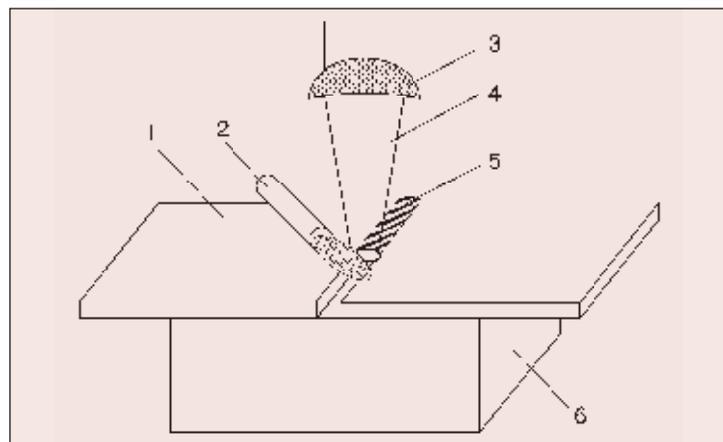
Технологическая схема лазерной сварки кромок стальных заготовок малой толщины, осуществляемая методом порошковой лазерной наплавки: 1 — свариваемые кромки; 2 — трубка для подачи присадочного порошка; 3 — фокусирующая линза; 4 — лазерное излучение; 5 — сварной шов; 6 — подкладка (стрелкой указано направление движения свариваемого изделия)
